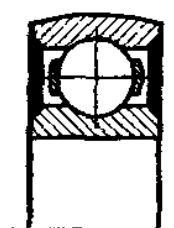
Шарикоподшипник со сферической поверхностью наружного кольца
